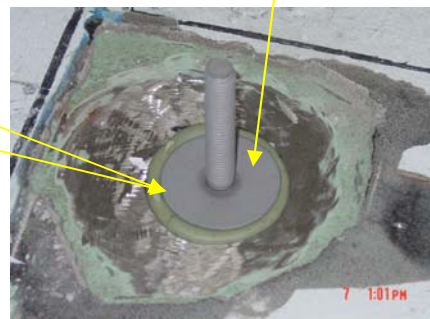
CB3200 Stehbolzen - wird als Befestigungselement für einen Sockel auf der „US Spica“ verwendet.
